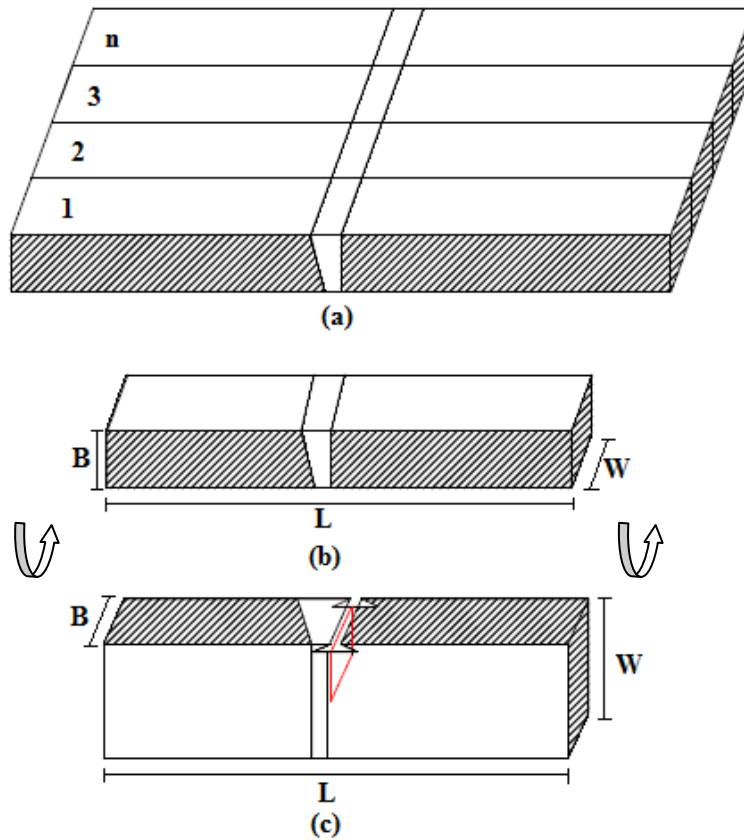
(a) Chapa soldada (b) Corpo-de-prova como fornecido (c) Posicionamento de entalhe na região de estudo. Sendo B = espessura, L = largura e W = altura.
